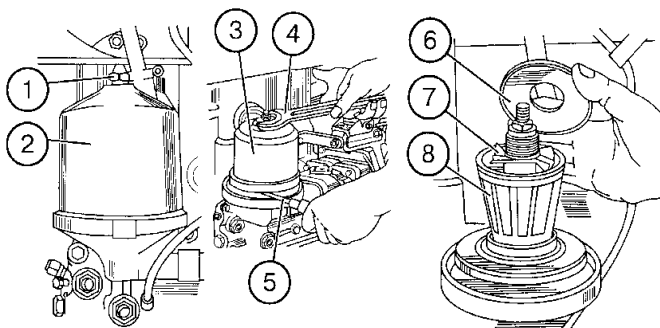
Очистка ротора центробежного масляного фильтра:
